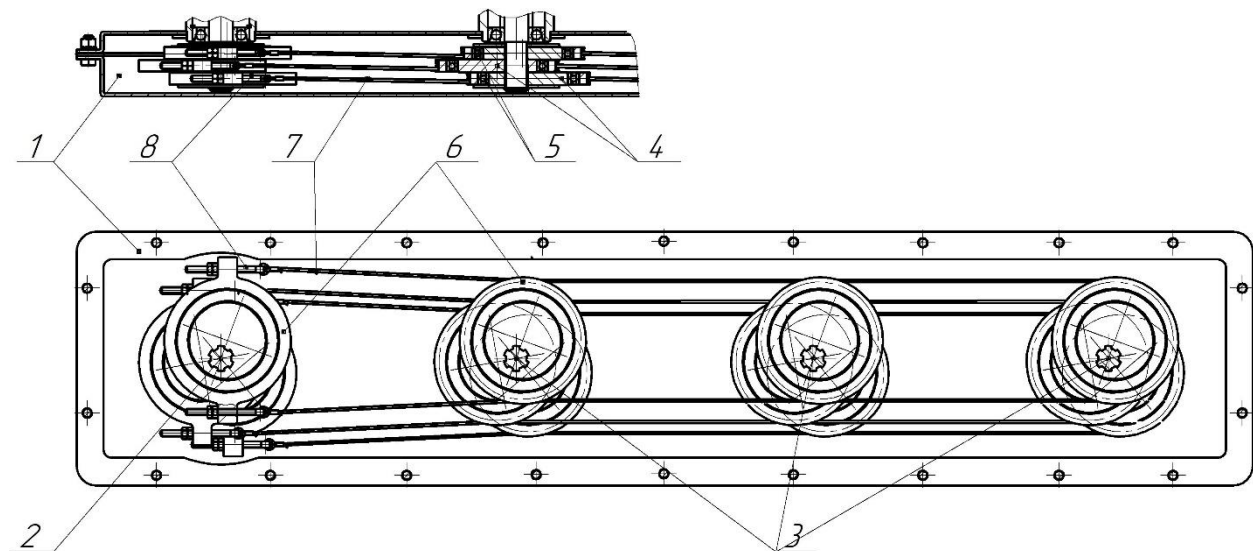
Паралелограмний механізм приводу бральних дисків: 1 – картер; 2 - ведучий вал; 3 – ведені вали; 4 – шківки-ексцентрики; 5 - підшипники; 6 - обойми; 7 – троси; 8 – натяжники
